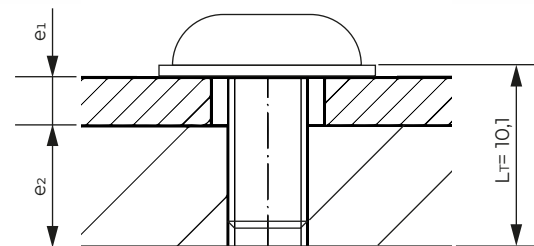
Unión 2 - Planteamiento inicial del montaje
